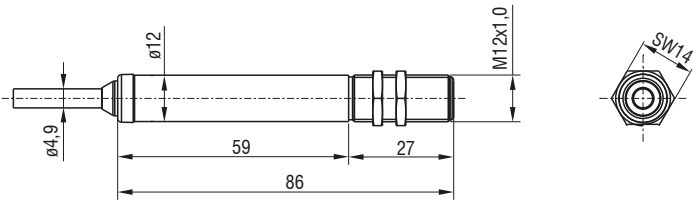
Maßzeichnung thermoMETER FI-SF15-C1, Abmessungen in mm
